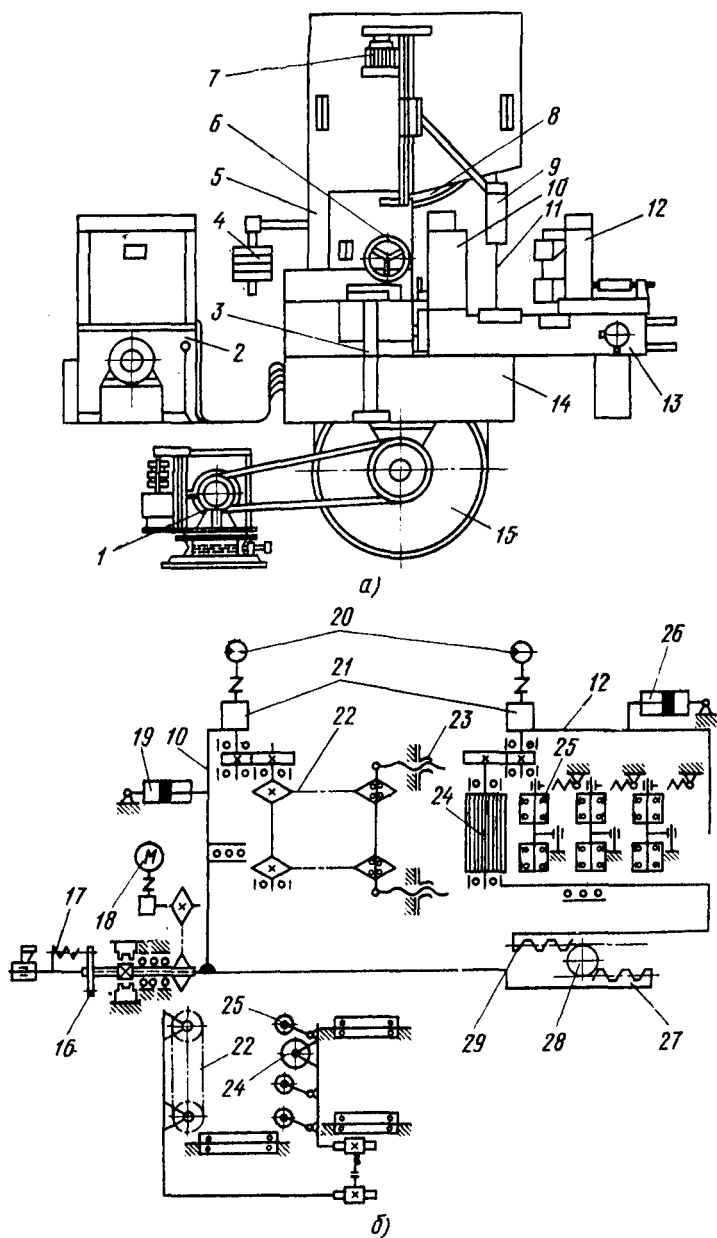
Делительный ленточнопильный станок ЛД125-2:
